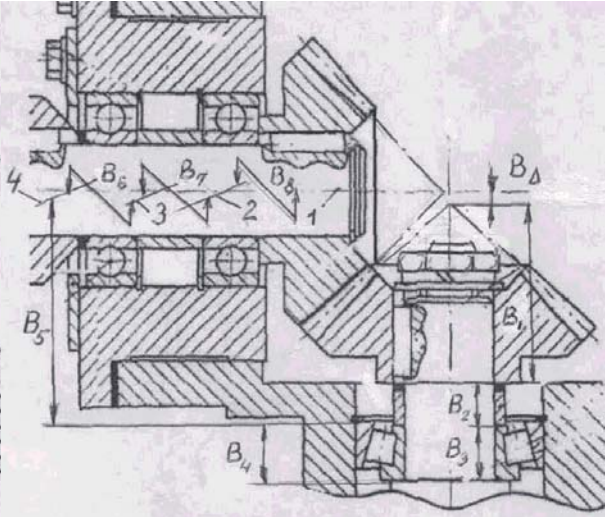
Схема размерной цепи B_{Δ} , определяющей совпадение вершин делительных конусов по вертикали: 1 – ось делительного конуса; 2 – ось отверстия колеса; 3 – ось опорной шейки вала; 4 – ось отверстия в корпусе
